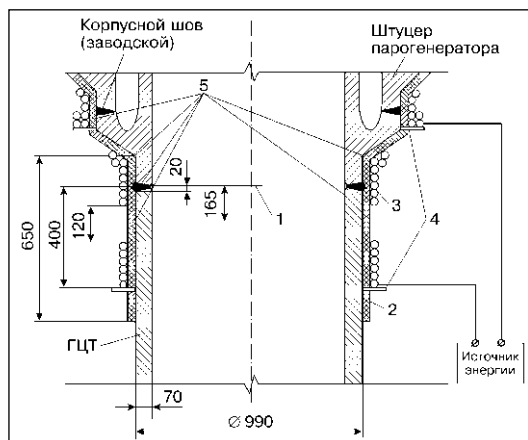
Схема укладки водоохлаждаемого индуктора: 1 — сварное соединение; 2 — теплоизоляция; 3 — водоохлаждаемый индуктор; 4 — штыри для крепления индуктора; 5 — места установки термопар
